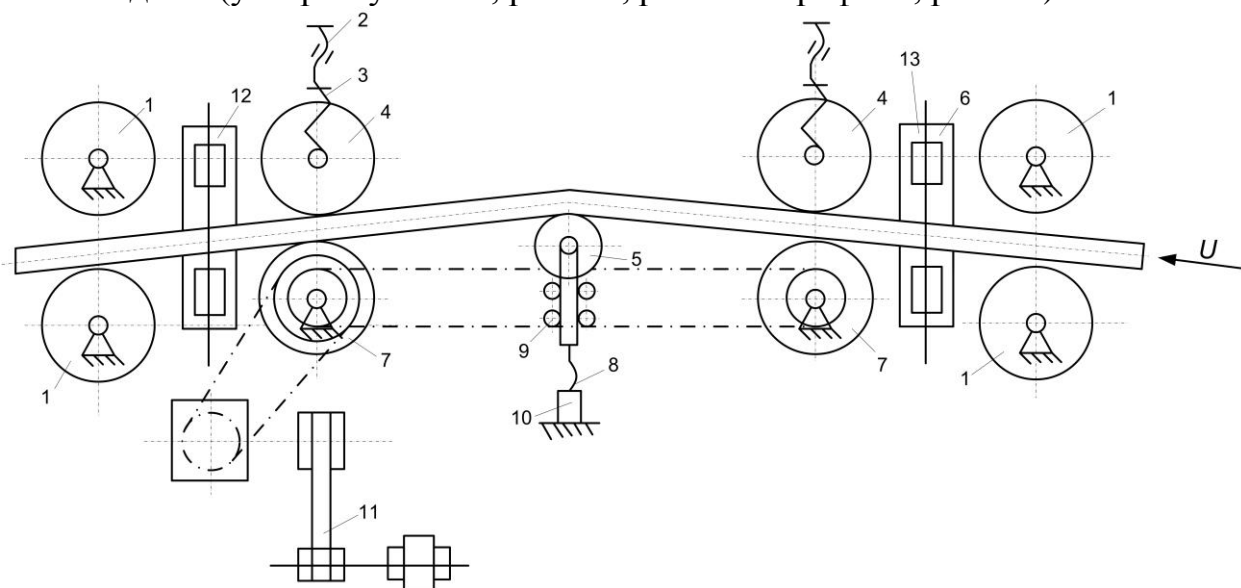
Кинематическая схема установки для сортировки пиломатериалов по модулю упругости 1 – направляющие вальцы; 2, 4 – подпружиненные вальцы; 3 – пружины; 5, 8 – изгибающий валец; 6 – поддерживающий валец; 7 – приводной валец; 9 – роликовые направляющие; 10 – преобразователь силы; 11 – привод; 12, 13 – фотореле.
